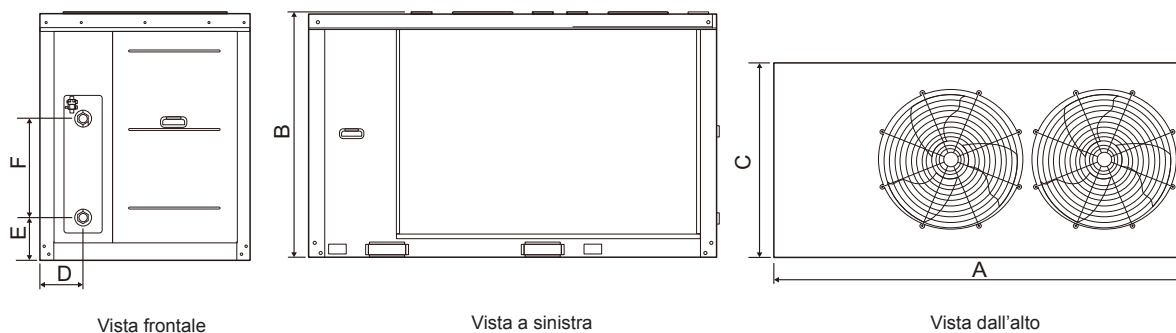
Dimensione d'insieme di KEM-60 DRS4.1
